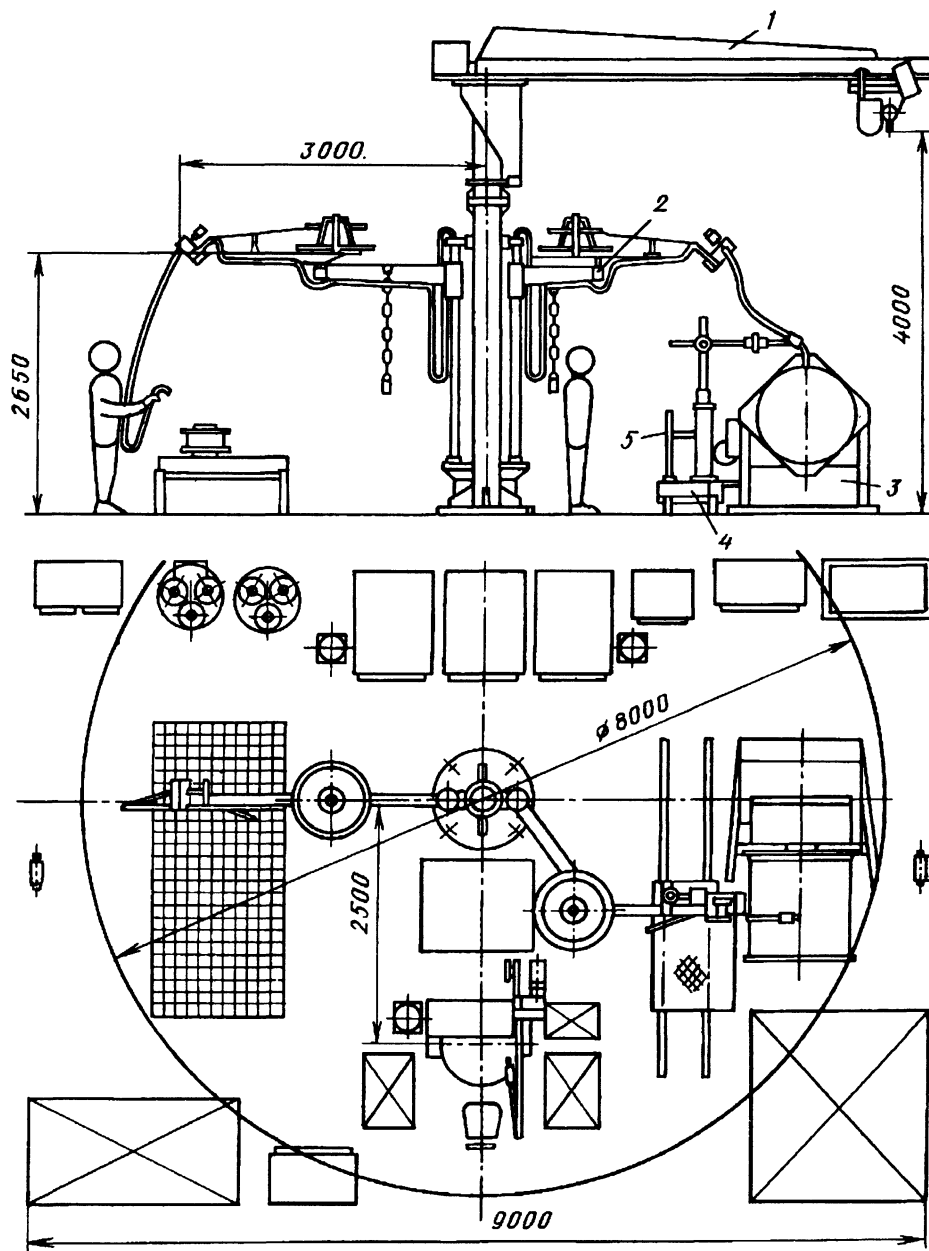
Типовой комплексно-механизированный трехпостовый участок УД246 для сборки и сварки плоских, пространственных, цилиндрических и малогабаритных изделий
